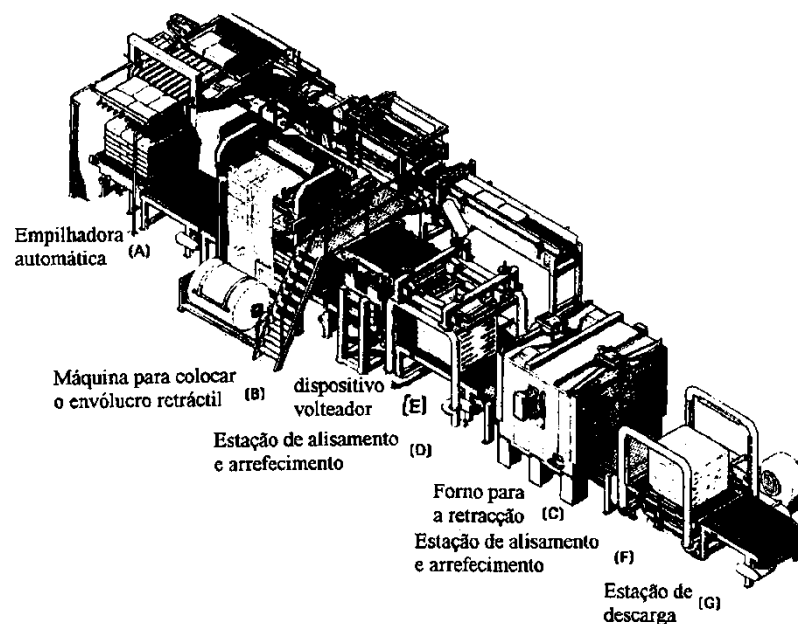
Instalação automática para a formação de pilhas de sacos ⁽³⁸⁾.
